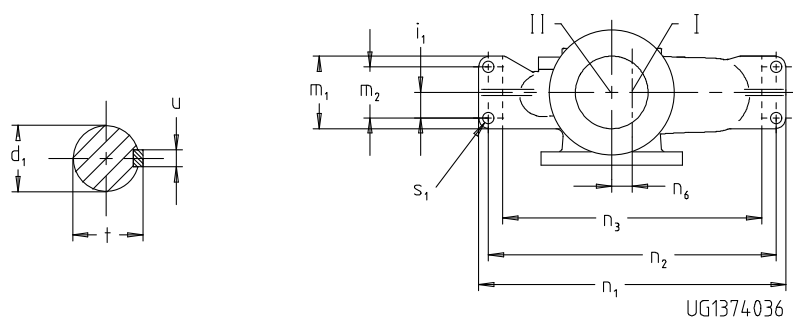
Размеры крепления по лапам и конца вала, дополнительные типоразмеры
